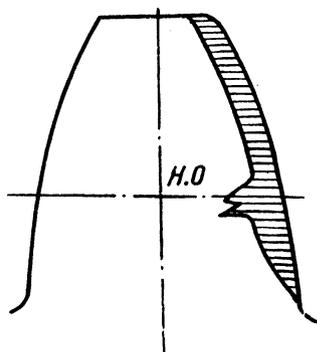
Схема износа поверхности профиля зуба [2] :
